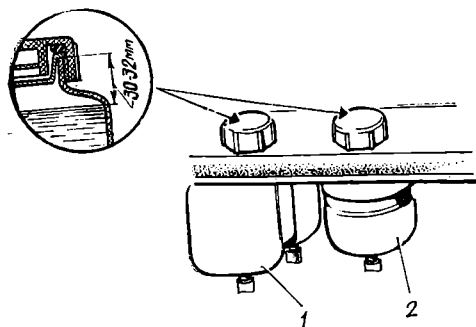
Питательные бачки главного цилиндра тормоза и главного цилиндра выключения сцепления (вид на бачки со стороны бажника):
